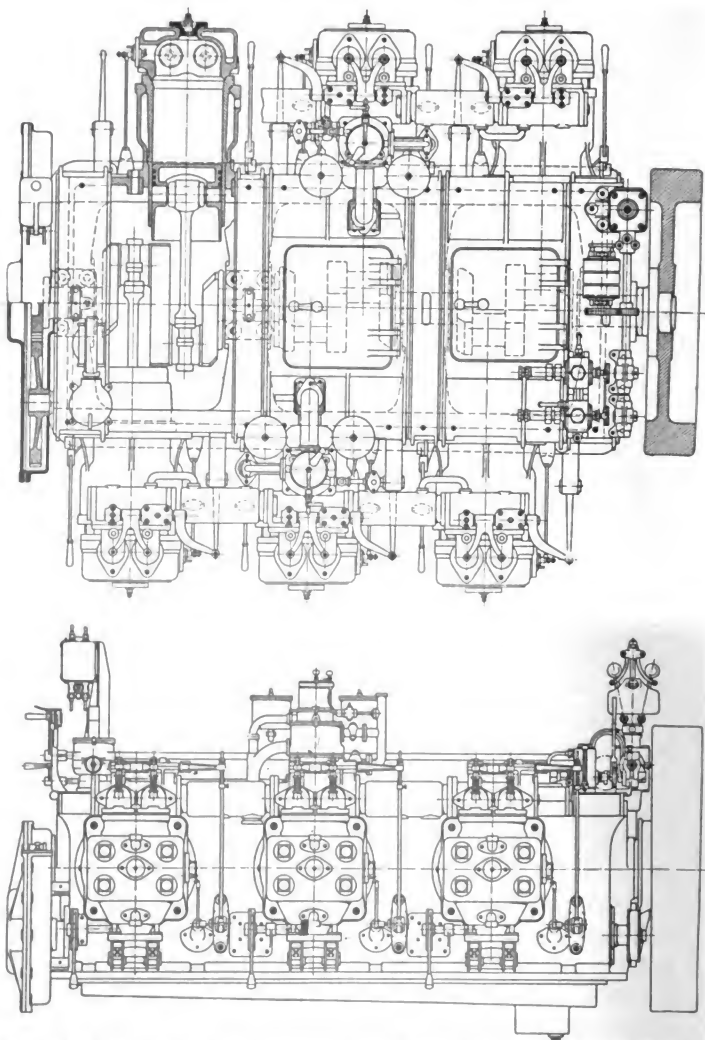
und 66. 140pferdiger Benzlnmotor der Wolseley Tool and Motor Car Works.
